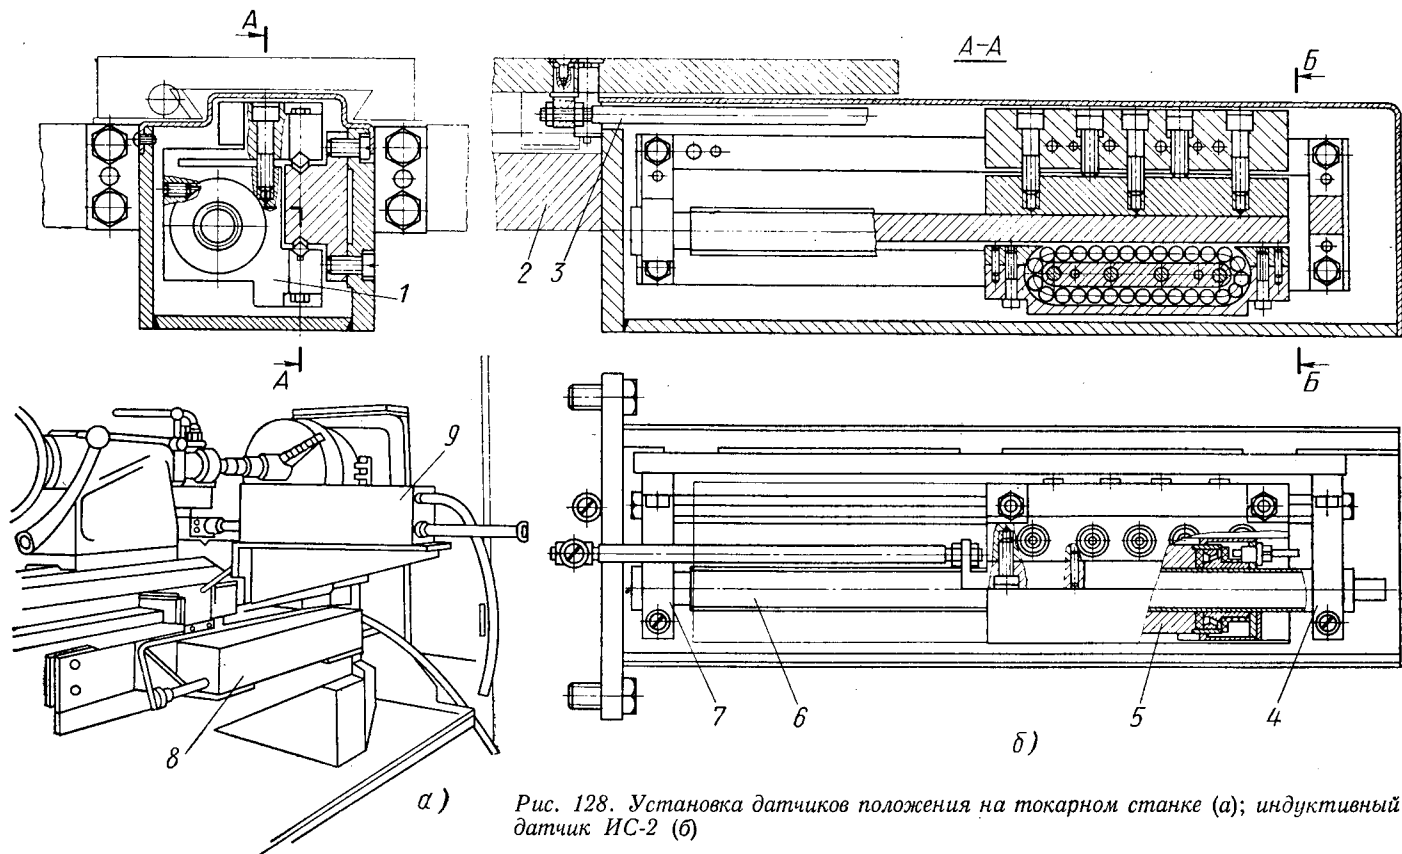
Установка датчиков положения на токарном станке (а); индуктивный датчик ИС-2 (б)
